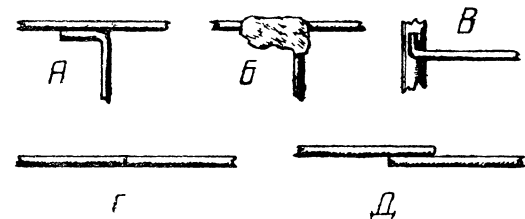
Способы соединения проводов пайкой. А — под углом; Б — заливка места соединения припоем, В — присоединение провода к лепестку детали, Г — встык, Д — накладка
